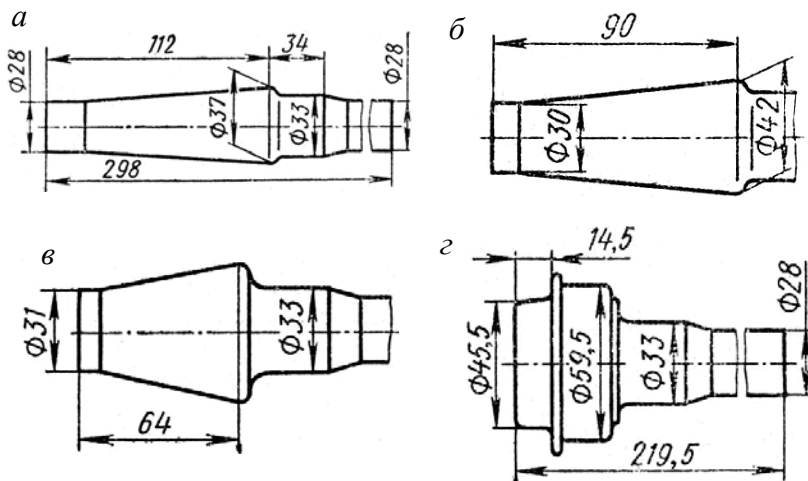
Набор металла (а – в) и высадка головки заготовки детали (г)
